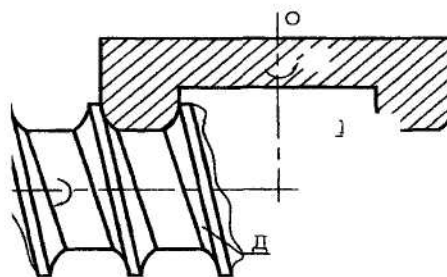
Кінематична схема обробки торцевими фрезами гвинтових поверхонь
